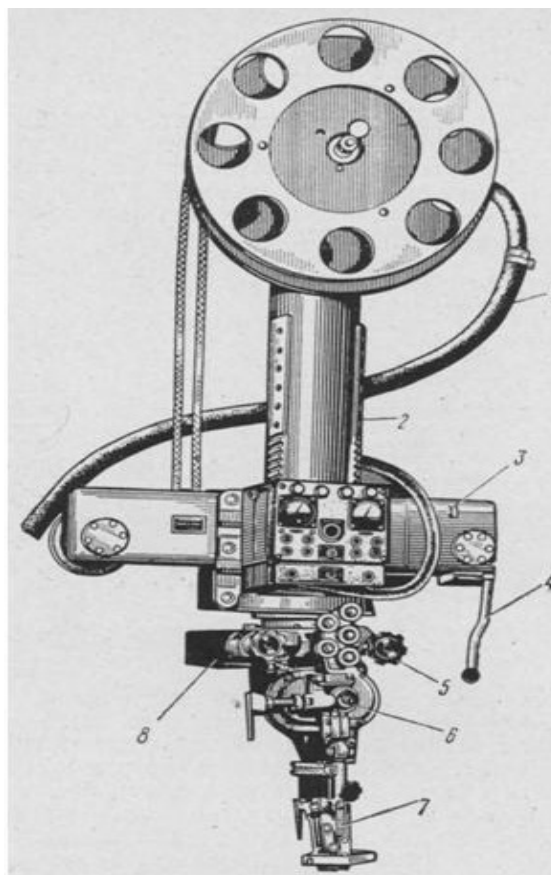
Конструктивные элементы автомата сварочного А-874
